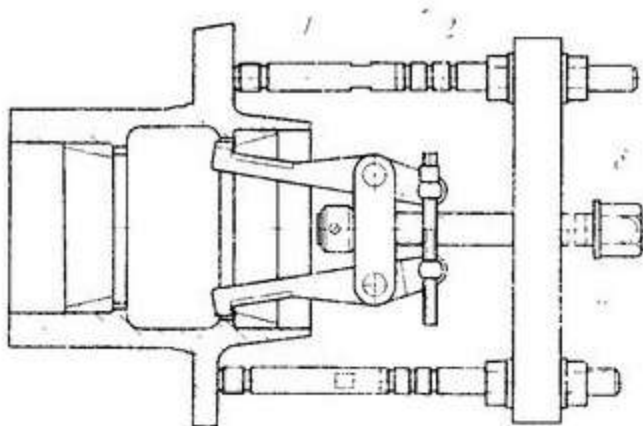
Выпрессовка наружного кольца подшипника ступицы
